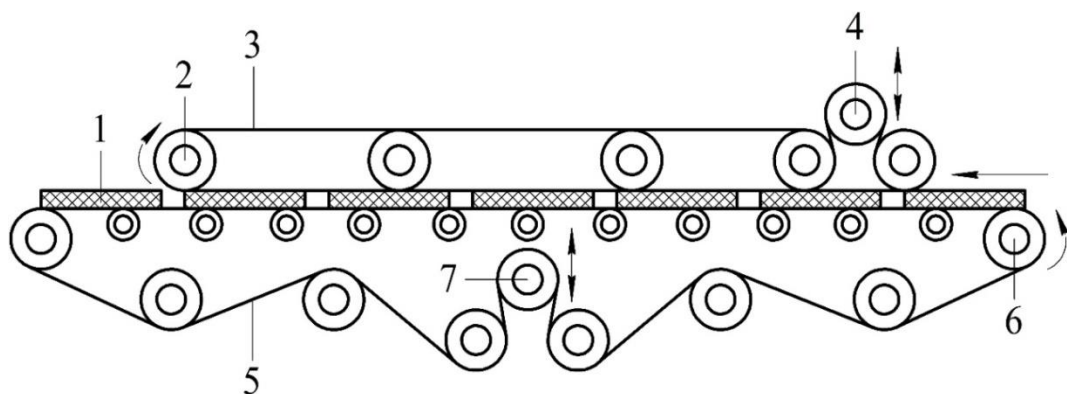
Кінематична схема механізму завершального каландрування, 1 – клеєні обкладинки після обтискання; 2, 6 – приводний вал; 3, 5 – транспортувальна багат шарова стрічка; 4, 7 – натяжні вали
